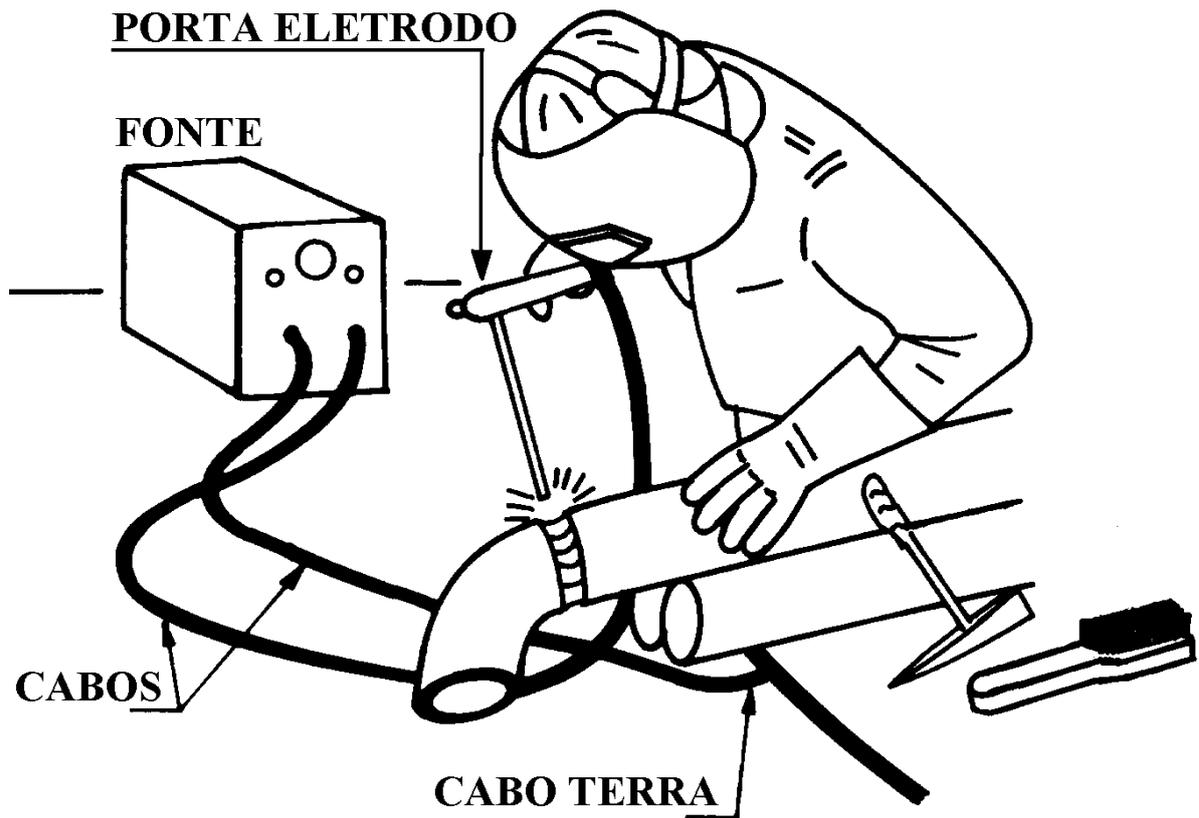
Equipamentos de Soldagem Eletrodos Revestidos.
